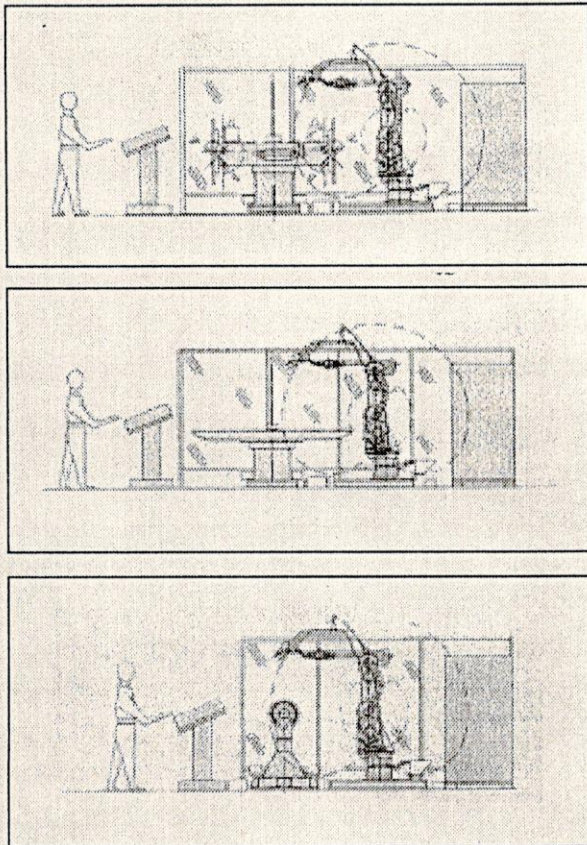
Ejemplos de celdas de soldadura (Gentileza de Rubén Constantini S.A.)
